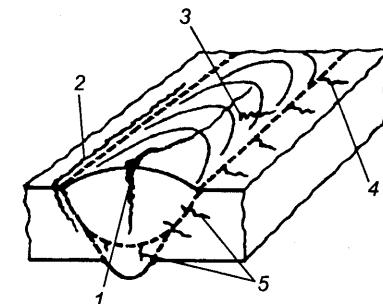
Расположение горячих трещин в сварных соединениях:
